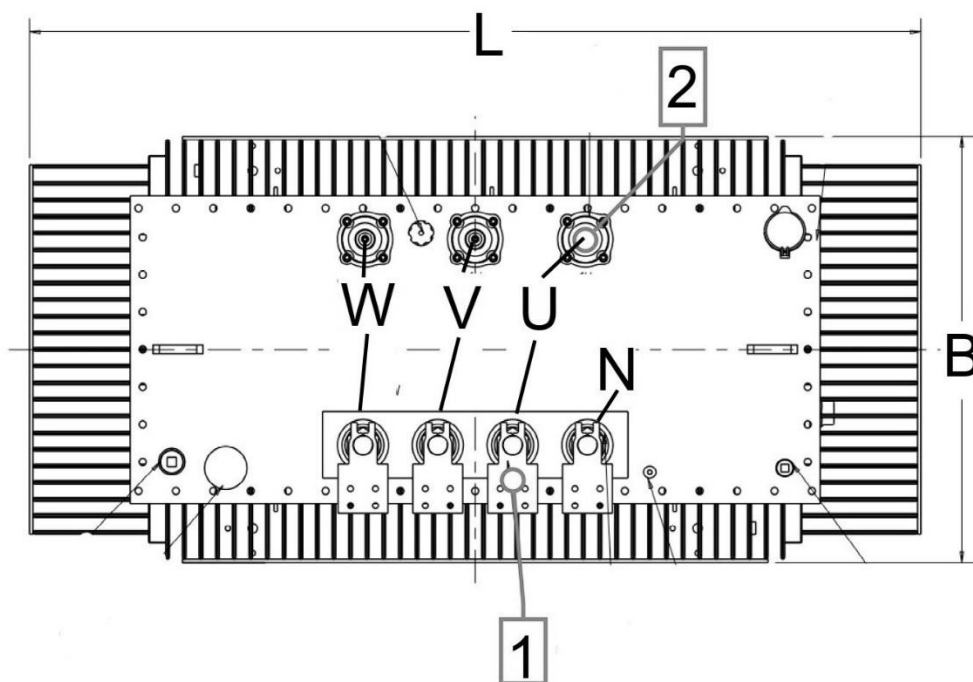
Draufsicht KNAN-Variante (Lage der Sensoren, Kühlrippen und Tank Design kann abweichen)
